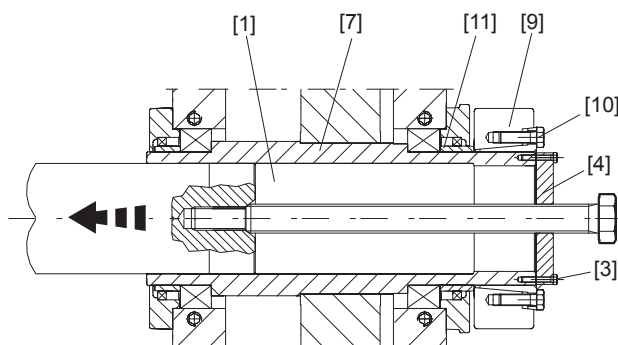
Réducteur horizontal avec frette de serrage monté
